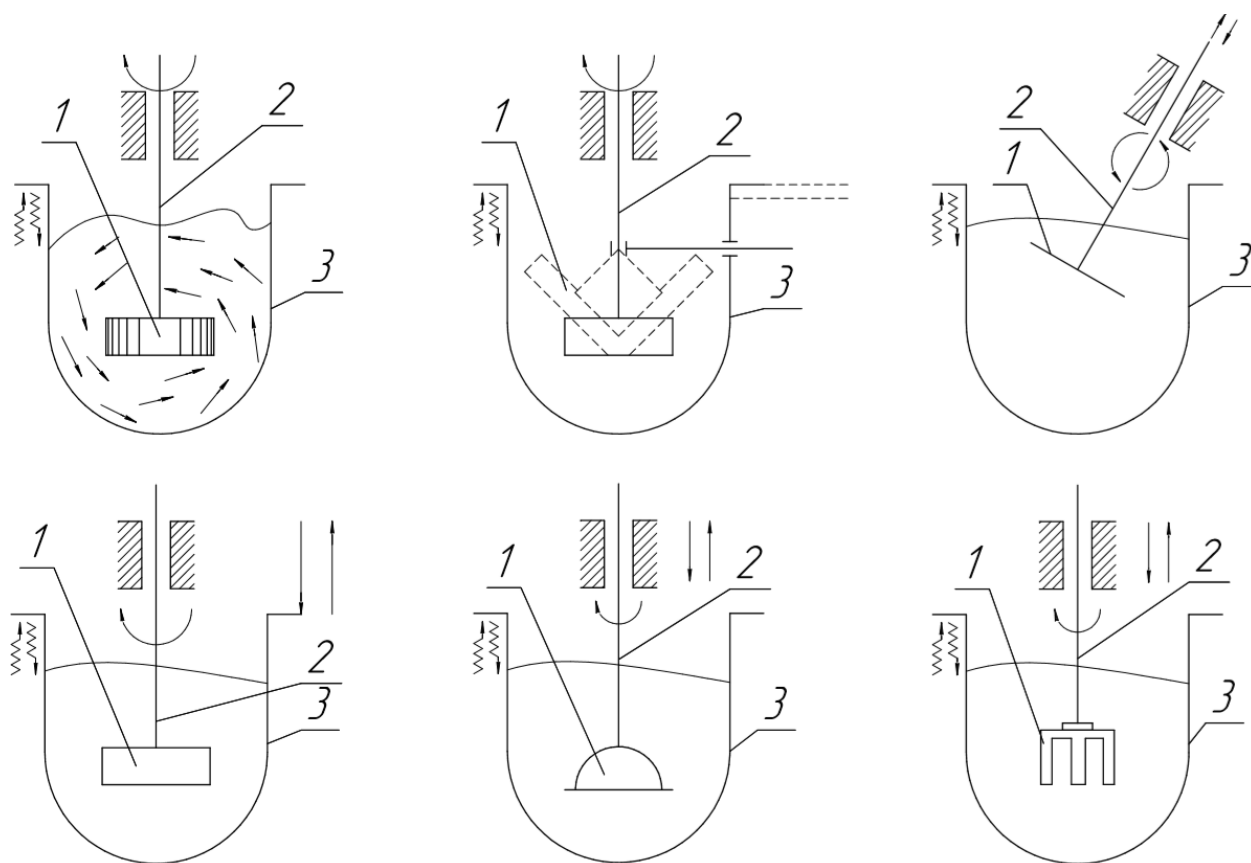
Схемы движений обрабатываемой детали, закрепленной на манипуляторе: 1 – обрабатываемая деталь; 2 – манипулятор; 3 – рабочий контейнер; — (сплошные стрелки) – главное направление движения; — (криволинейные) – направление движения подачи
